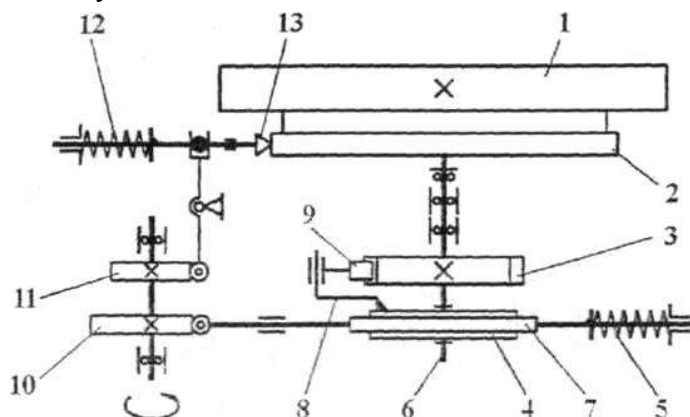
Кінематична схема приводу каруселі з храповим механізмом: 1 – карусель; 2 – диск фіксатора; 3 – храпове колесо; 4 і 7 – колесо і рейка зубчато-рейкового механізму; 5 і 12 – пружини; 6 – вал; 8 – водило; 9 – собачка; 10 і 11 – кулачки приводу відповідно рейки зубчато-рейкового механізму і фіксатора; 13 – фіксатор
